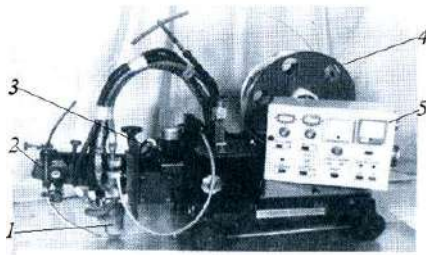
Сварочный автомат для плазменно-дуговой сварки изделий
